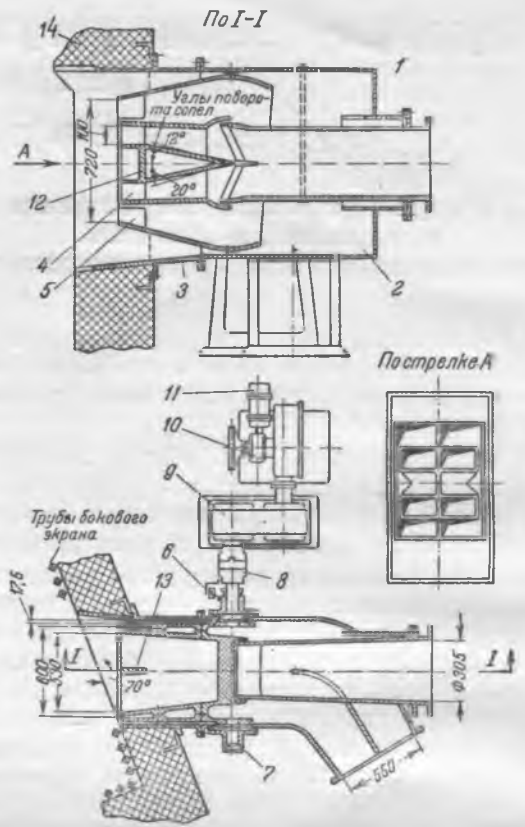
Поворотная горелка первой конструкции (УП-1). 1 — короб первичного воздуха; 2 — короб вторичного воздуха; 3 — корпус горелки; 4 — сопло первичного воздуха; 5 — сопло вторичного воздуха; 6 — указатель поворота; 7 — цапфы; 8 — соединительная муфта; 9 — редуктор; 10 — колодка дистанционного управления с редуктором; 11 — электродвигатель; 12 — рассекатель; 13 — клинья; 14 — амбразура.
